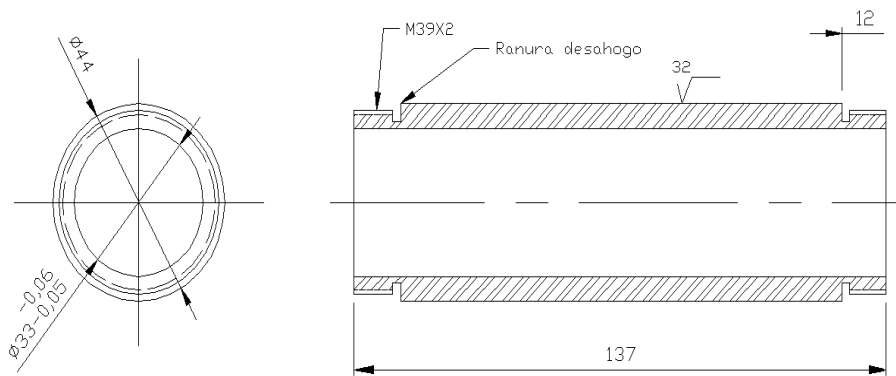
Sección transversal del contenedor y de la tapa externa del crisol, dimensiones propuestas en milímetros.
